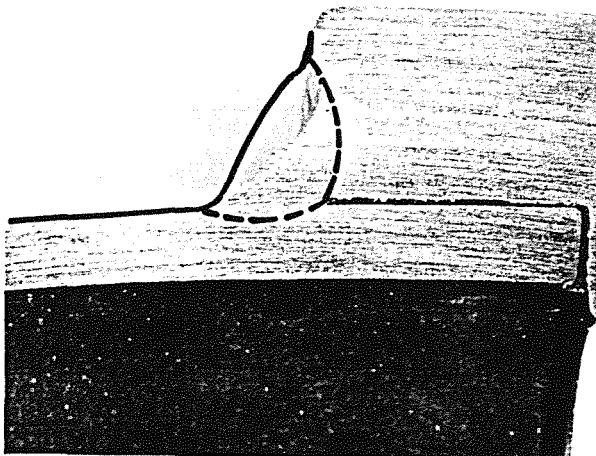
Sección de la soldadura de un conector suministrado por la Empresa A. Se aprecian mordeduras y falta de material de aporte. Se ha marcado, además, el perfil ideal del cordón de soldadura.
